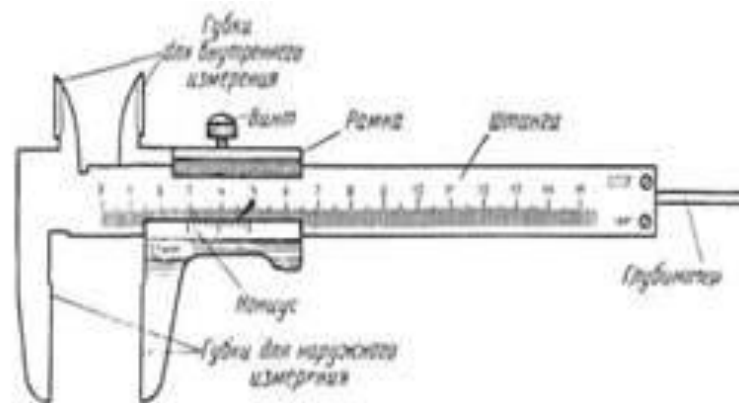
Устройство штангенциркуля ШЦ-I 0-125 0.1 ГОСТ 166-80
